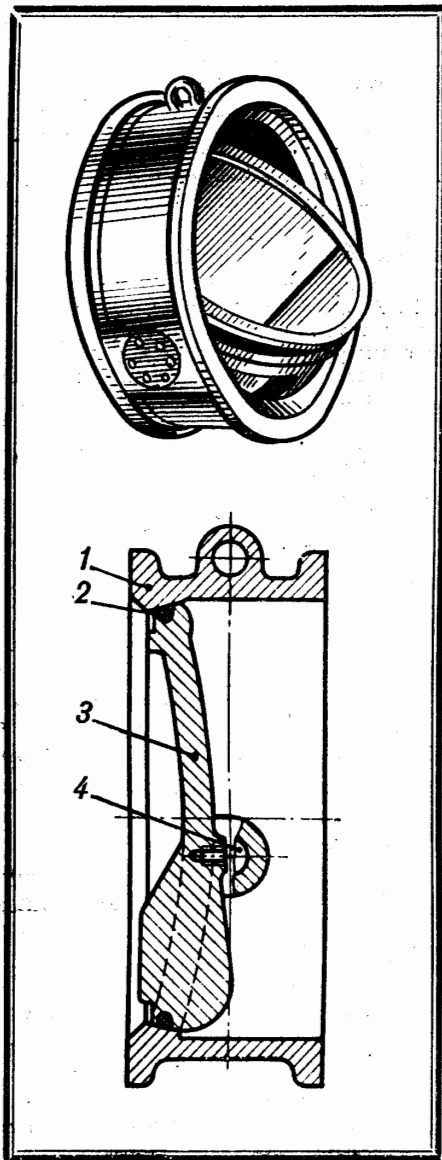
Клапан-автомат и его схема: 1 — корпус, 2 — уплотнитель, 3 — диск-клапан, 4 — ось.
